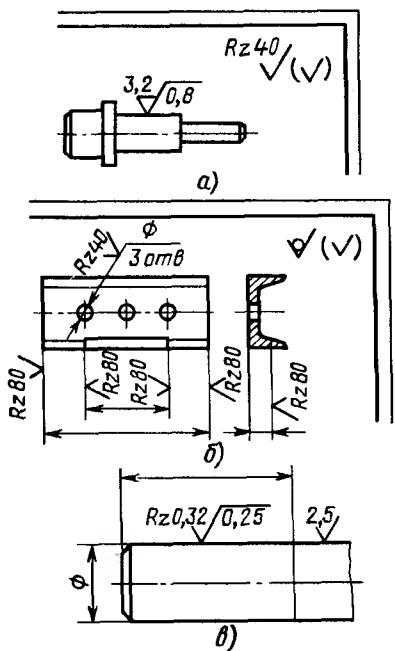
Обозначения шероховатости поверхностей на чертежах:
